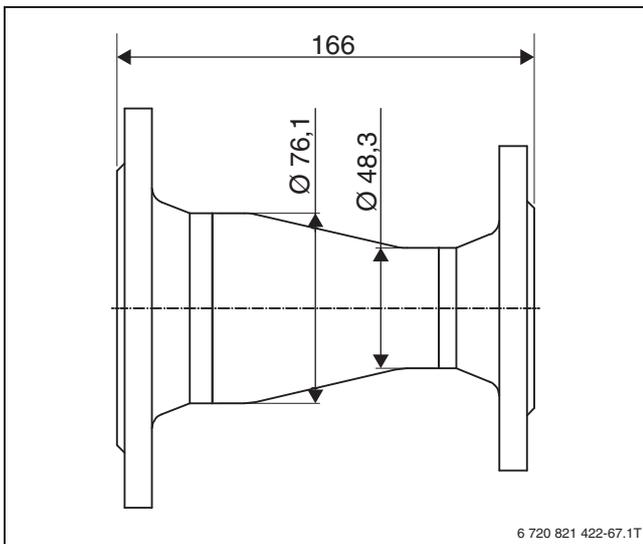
Übergangsstück DN 65/PN 6 – DN 40/PN 6 (Maße in mm)
